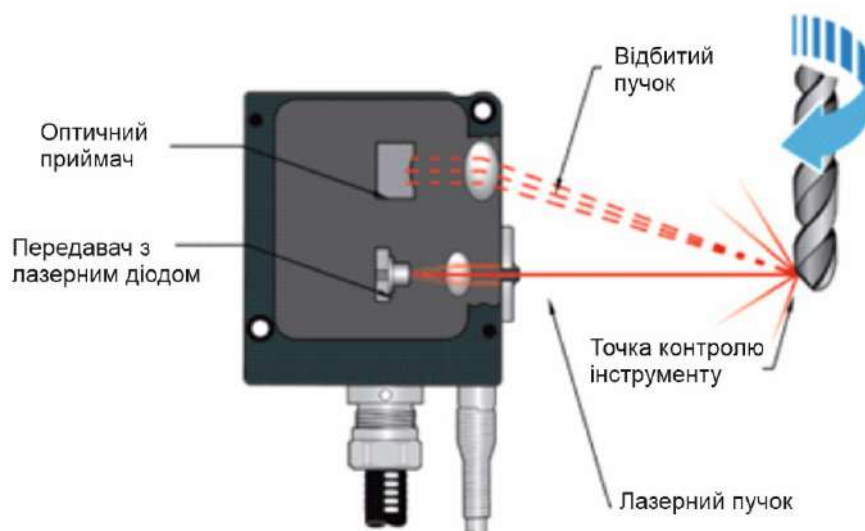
Схема роботи лазерної одномодульної системи для виявлення несправного інструменту
